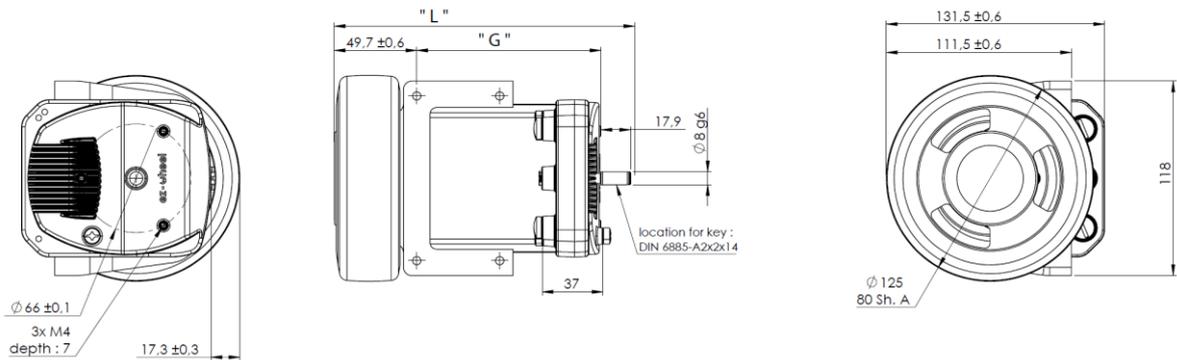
Dimensions hors tout - SWD<sup>®</sup> Core - avec frein externe
